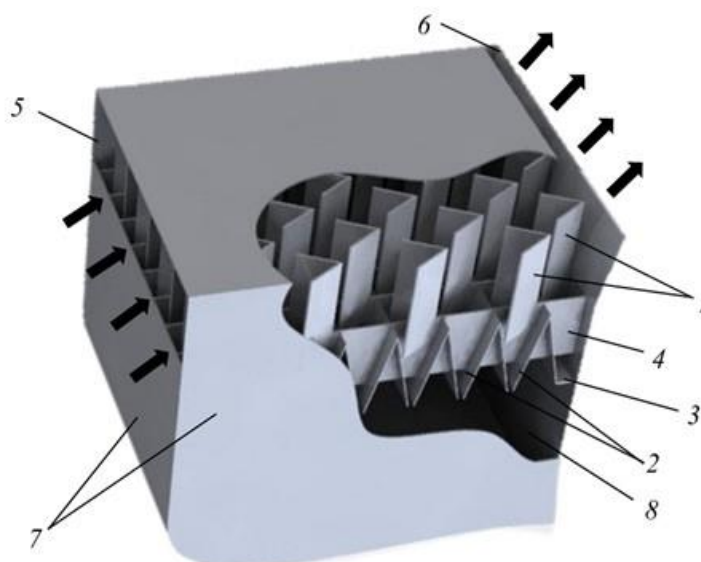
Трехмерная модель устройства: 1 – сепарационные элементы; 2 – сепарирующая решетка; 3 – пластина; 4 – перпендикулярная пластина; 5 – входной патрубок; 6 – выходной патрубок; 7 – корпус; 8 – пылесборный бункер
